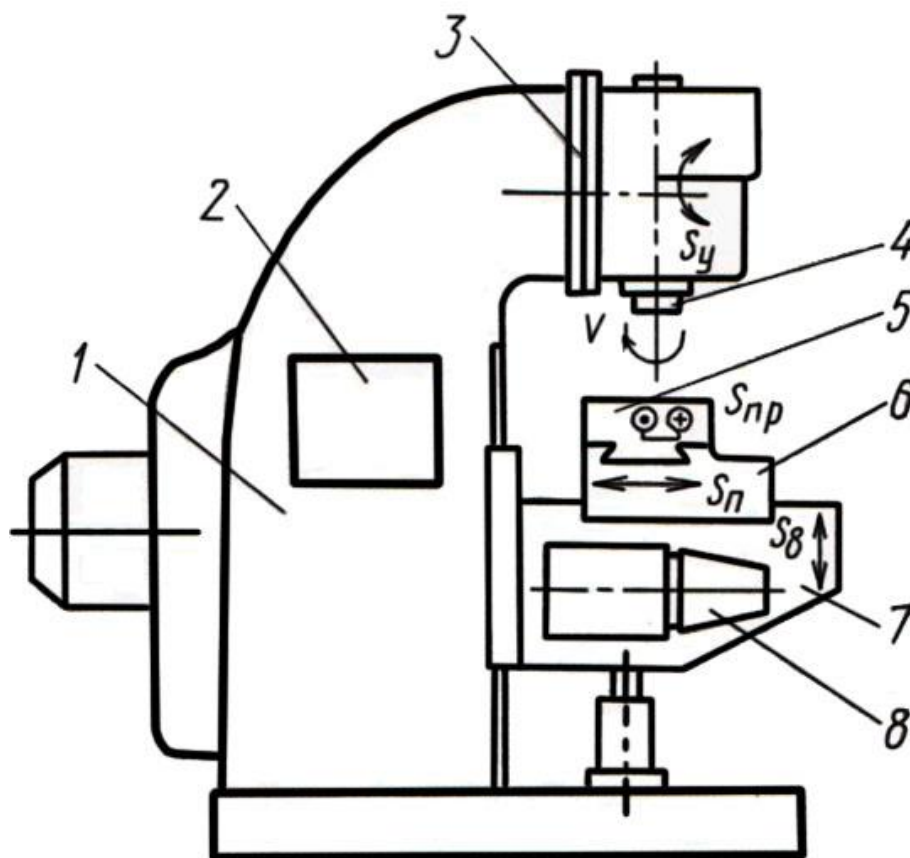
2. Общий вид вертикально-фрезерного станка:
